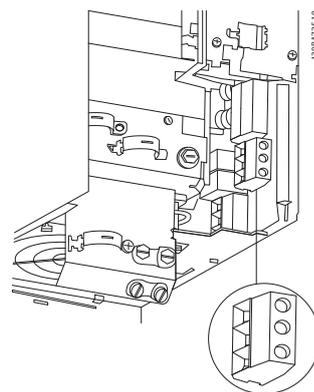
Type de protection du raccordement au secteur B3 (IP20)
